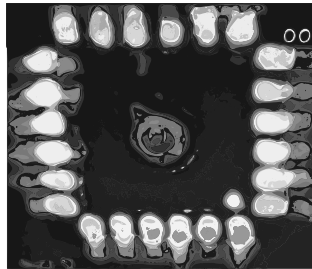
Alineación entre la placa y la pastilla a soldar.
